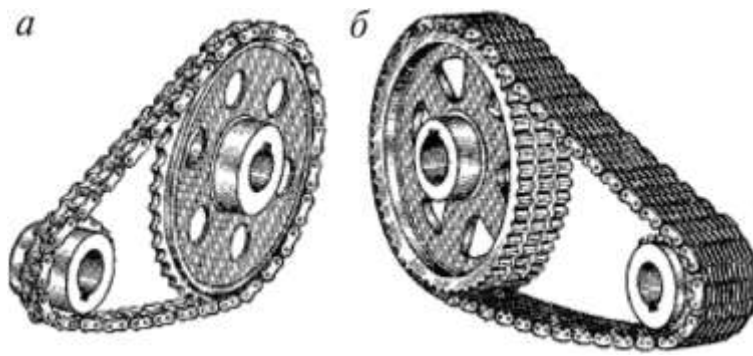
Цепная передача роликовой (а) и зубчатой (б) цепью
